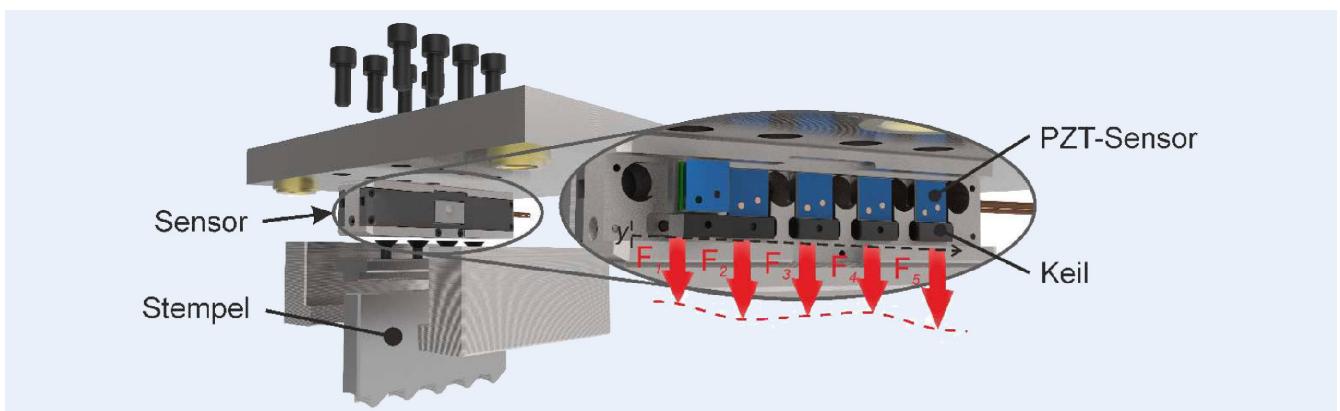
Linienkraftmessung an einem Kerbwerkzeug. Grafik: Fraunhofer IWU
